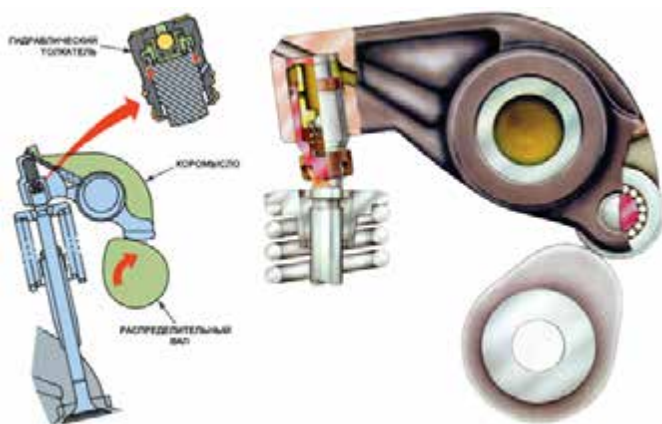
Гидравлический механизм регулировки теплового зазора (HLA) встроен в коромысло двигателя с распределительным валом, расположенным в головке цилиндров. Для корректной работы подобного механизма очень важна правильная подборка моторного масла по вязкости (SAE-рейтинг); источник: *Pearson Education, Inc. u INA
